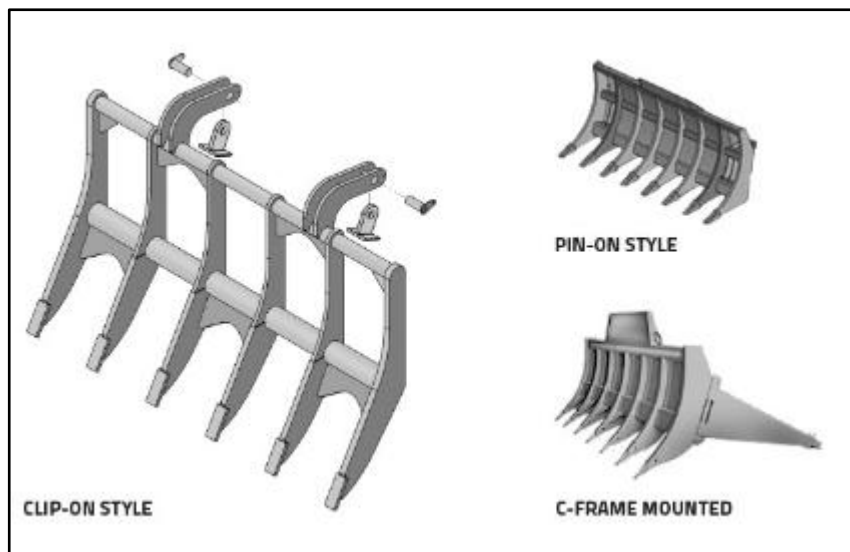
Lâmina "Brush" – Fonte: Weldco beales, 2025.
